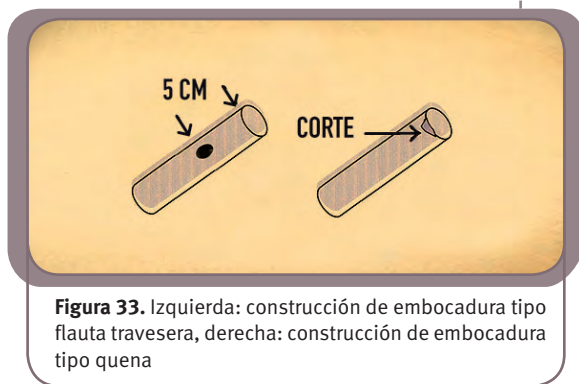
Izquierda: construcción de embocadura tipo flauta travesera, derecha: construcción de embocadura tipo quena
